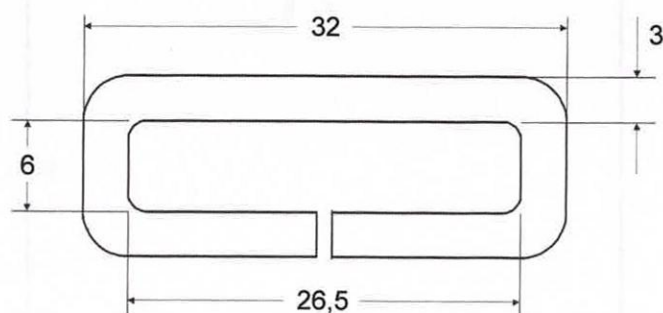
Vista da argola retangular do tirante inferior (medidas em mm)
